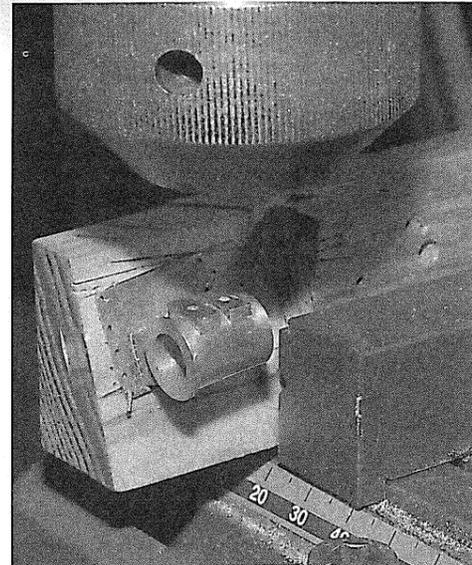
fixation d'une barre de 8 x 4 sur le plateau tournant avant (en réalité après...) creusement à la fraiseuse. Le trou à l'extrémité de la barre correspond à un de ceux que l'on voit sur la photo 3 ci-contre, qui servent à visser les pièces au cylindre avant la soudure qui précède l'usinage définitif, puisqu'il faut alors avoir enlevé les vis.
